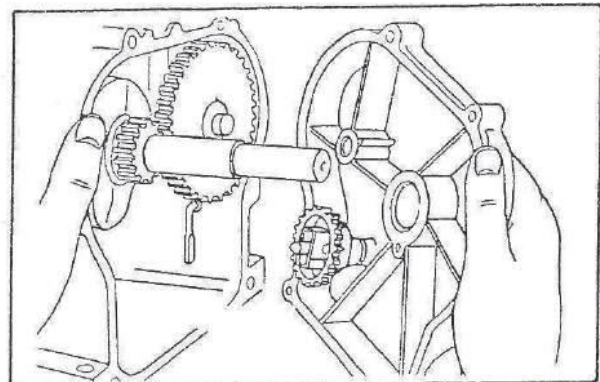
Assemblage du flasque avec le régulateur montrant le bras du régulateur en position correcte
